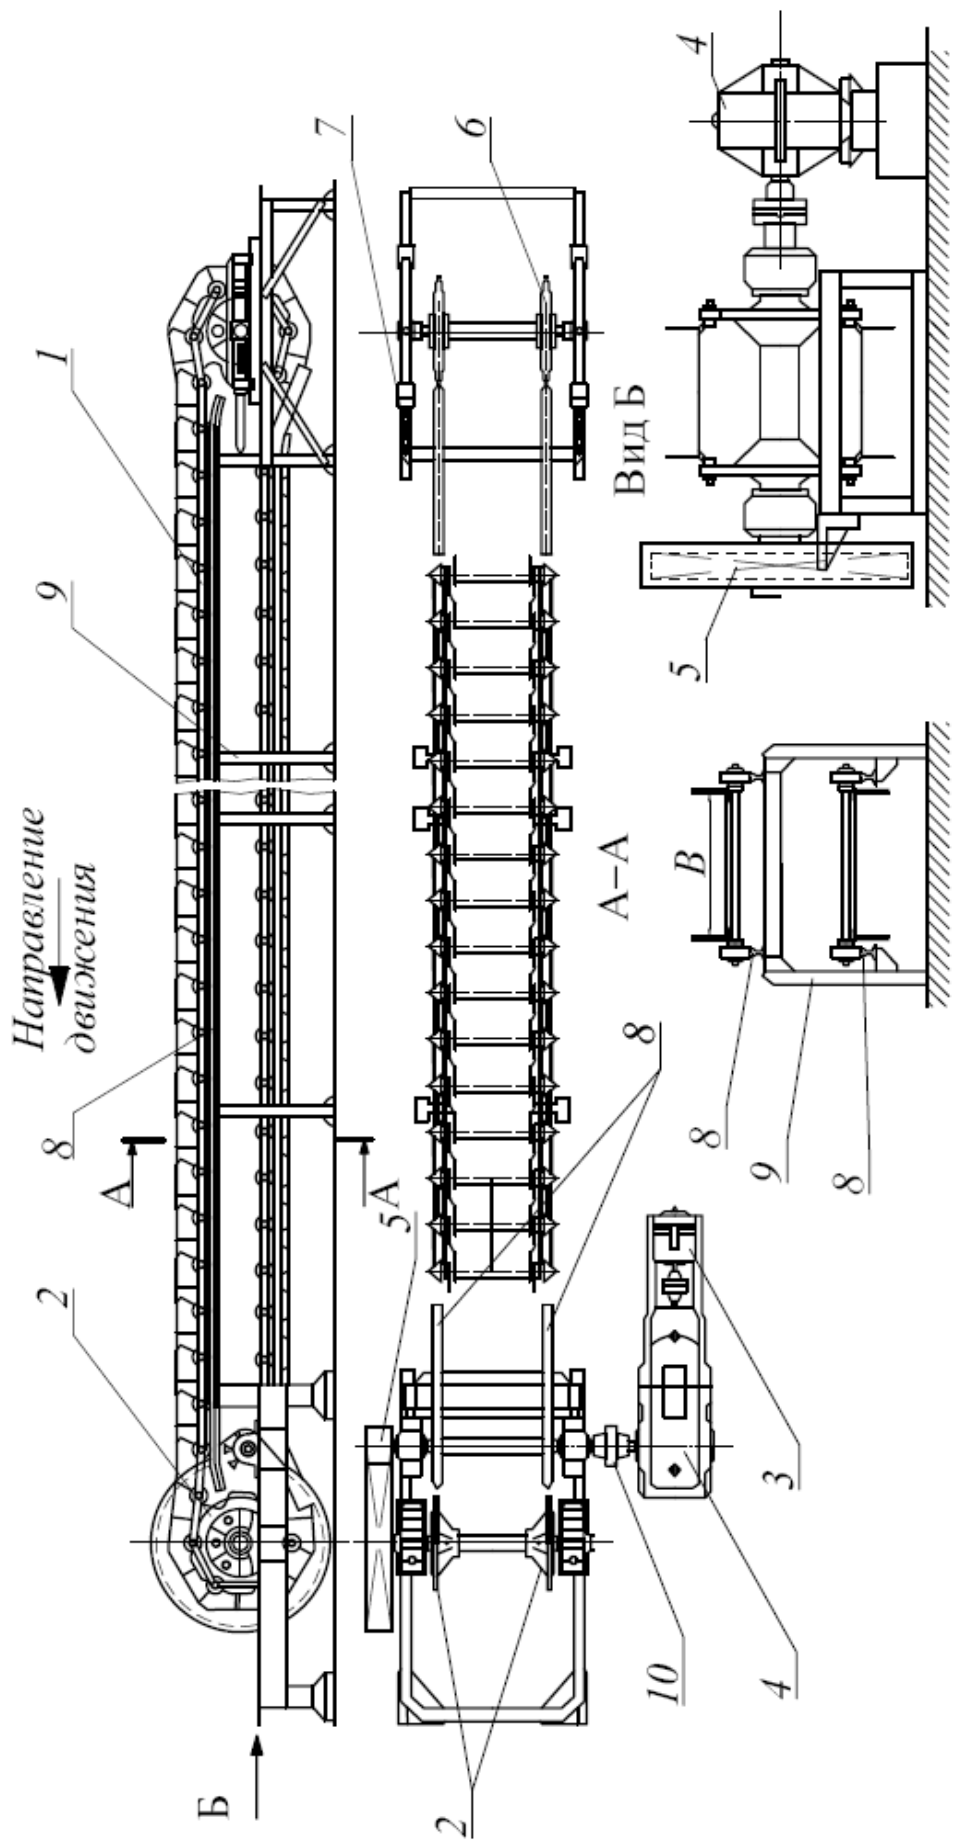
Пластинчатый конвейер: 1 – ходовая часть конвейера с двумя тяговыми цепями; 2 – приводные звездочки; 3 – электродвигатель; 4 – редуктор; 5 – открытая зубчатая передача; 6 – хвостовые звездочки; 7 – натяжное устройство; 8 – направляющие шины; 9 – станина конвейера; 10 – втулочно-пальцевая муфта
